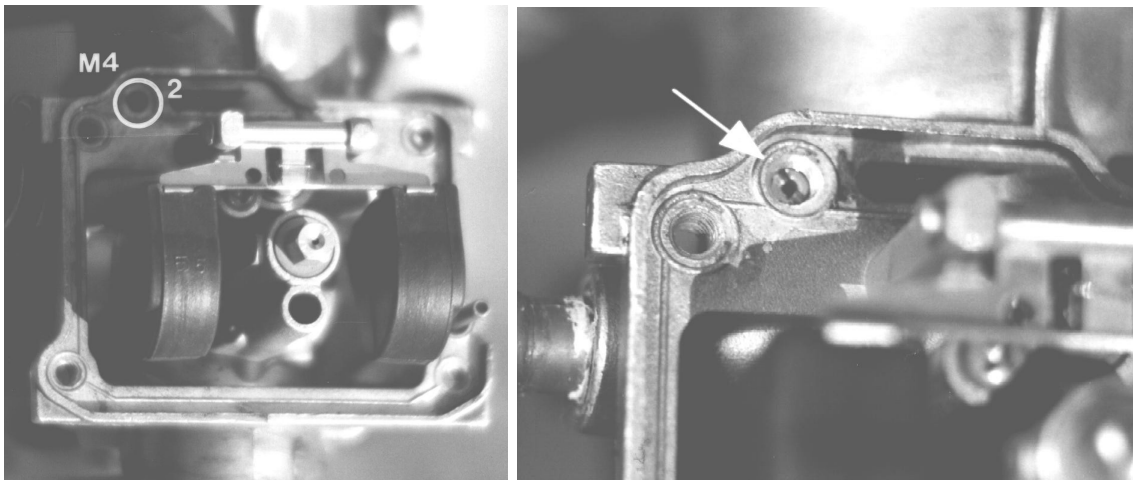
Gewinde M4 für Power-Jet (Links: Serie; Rechts: Umbau)
